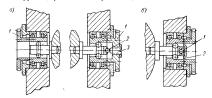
Схемы крепления разновращающихся подшипников без внутренних колец
